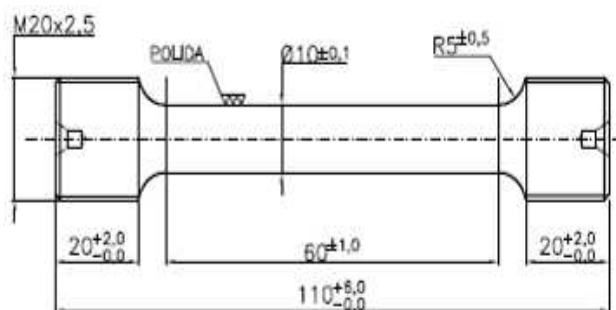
Desenho sem escala do corpo-de-prova utilizado nos ensaios de tração. Dimensões em mm.
